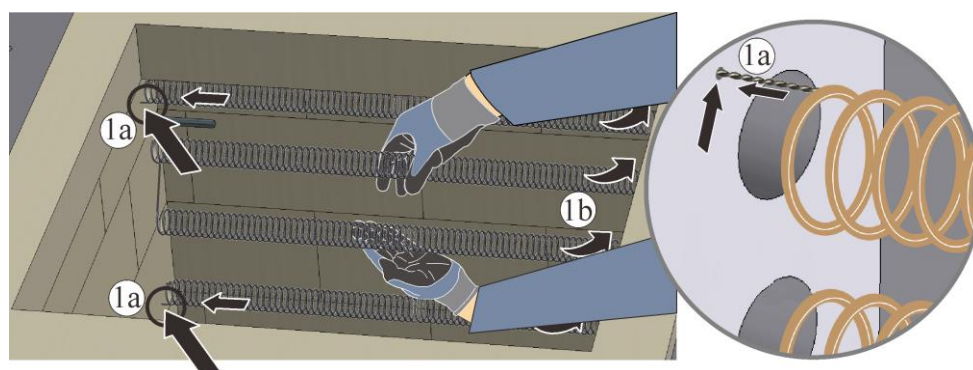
Установка нагревательных элементов (рисунок примерный)
